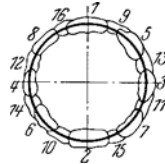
Reihenfolge beim Schweißen auf eine Welle.
